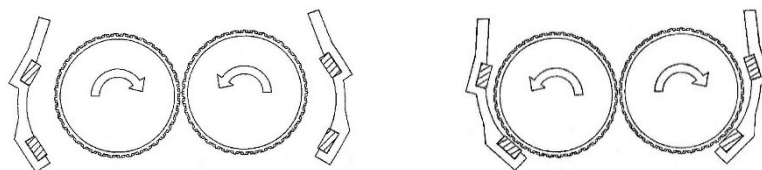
Схема робочої зони двовалкової дробарки за заявкою № WO03/045561A1
